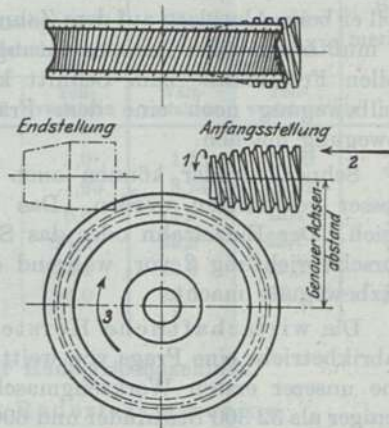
und 617. Fräsen der Schneckenräder mit kegeligem Fräser.
